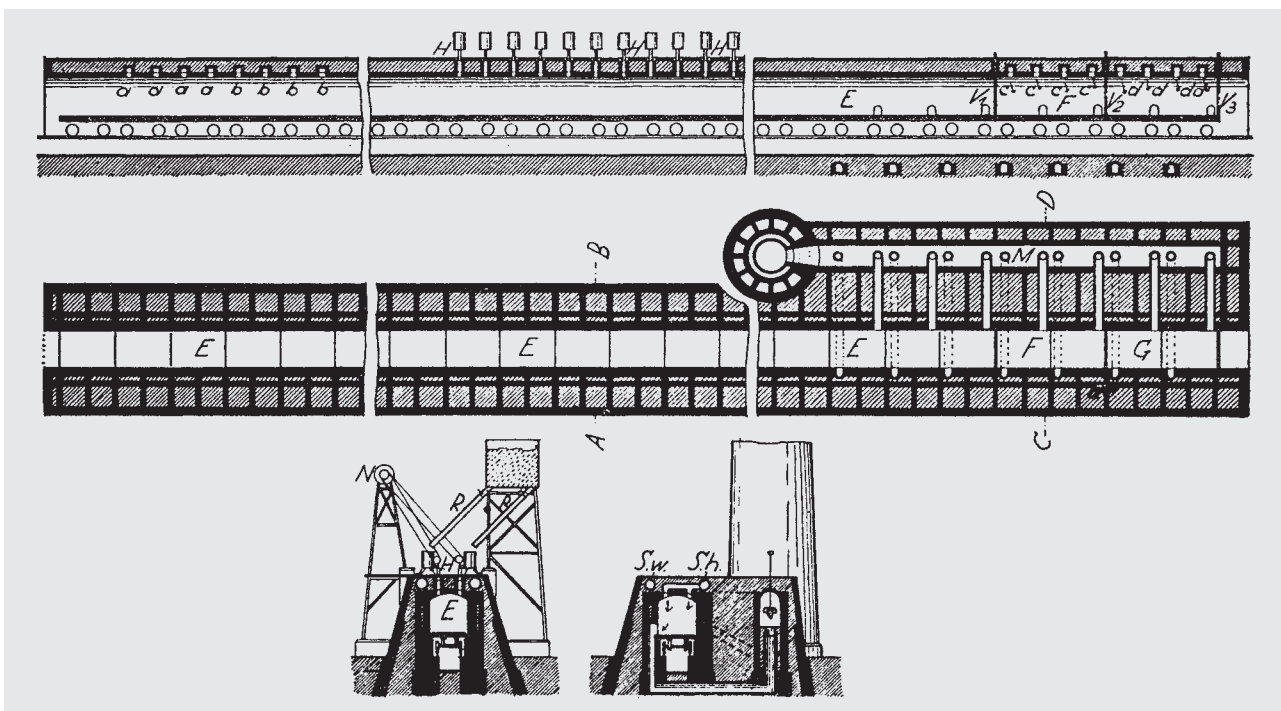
Tunnelofen mit Kohle-Streufeuerung durch Schüttlöcher in der Ofendecke
